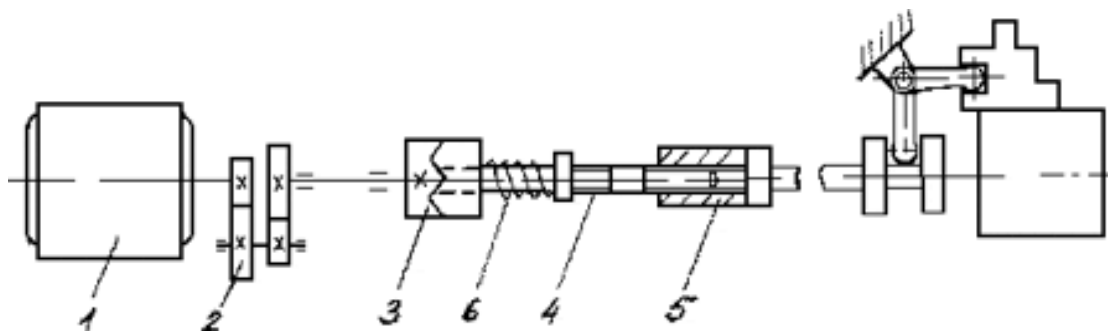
Затискний пристрій з приводом від електродвигуна
